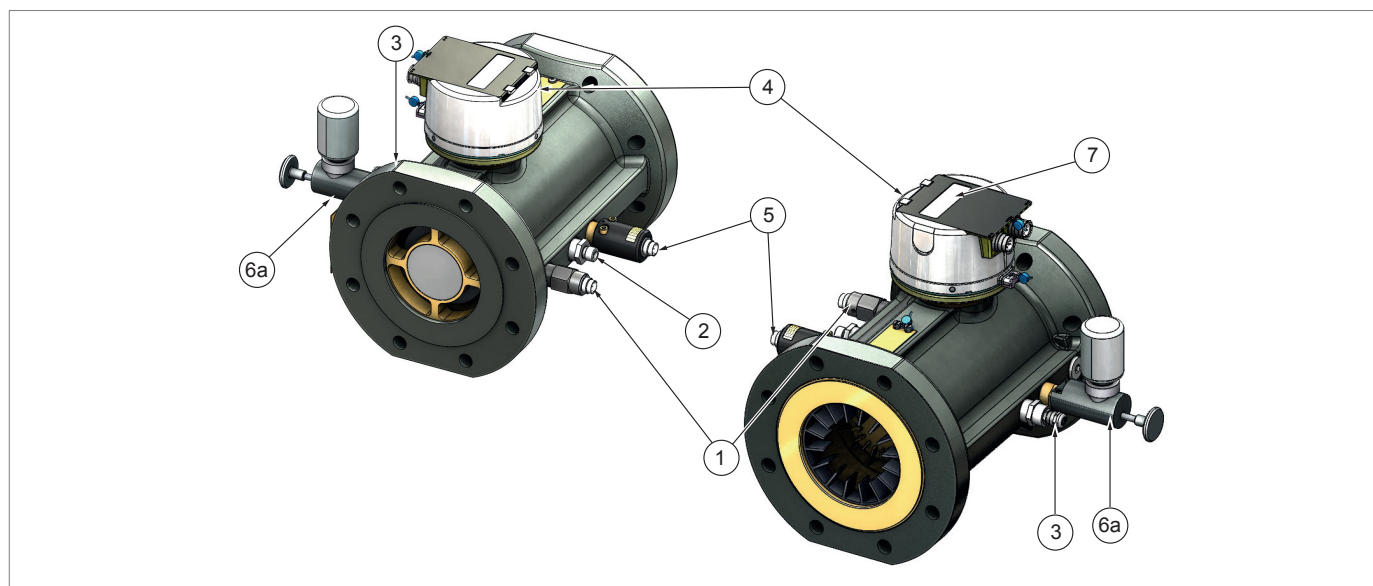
Positionnement des raccords et des accessoires du compteur iM-TM corps en aluminium
